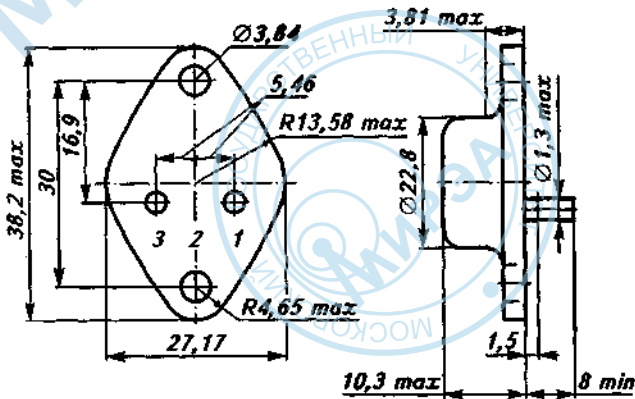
Общий вид, габаритные и присоединительные размеры транзисторов КТ827А и КТ945А в корпусе КТ-9:
